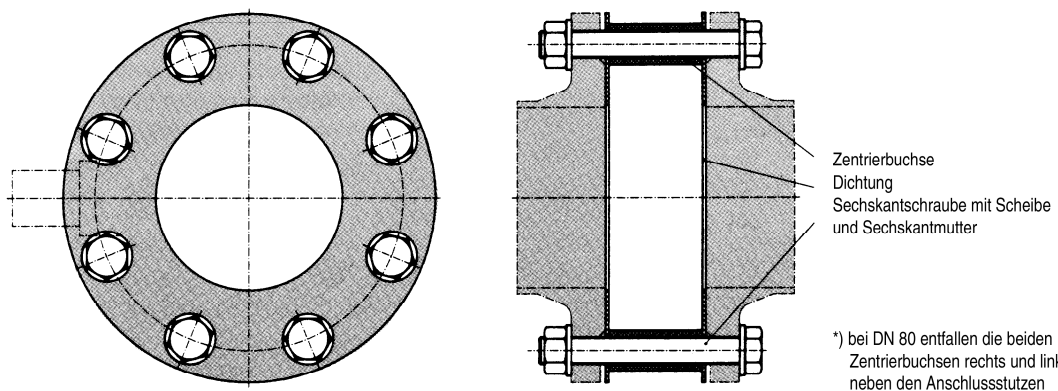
Zentrierbausatz (nur für Zwischenflansch Ausführung)
